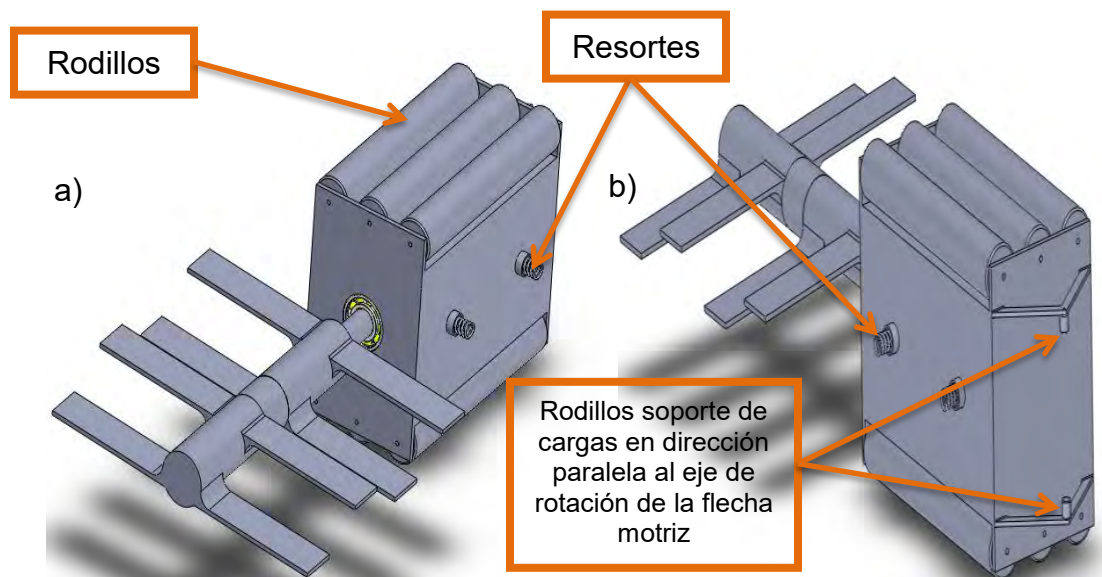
Conjunto motor, a) Vista en 3D detalle la colocación de la flecha motriz y frente del conjunto, b) Vista de la parte posterior del conjunto motor
